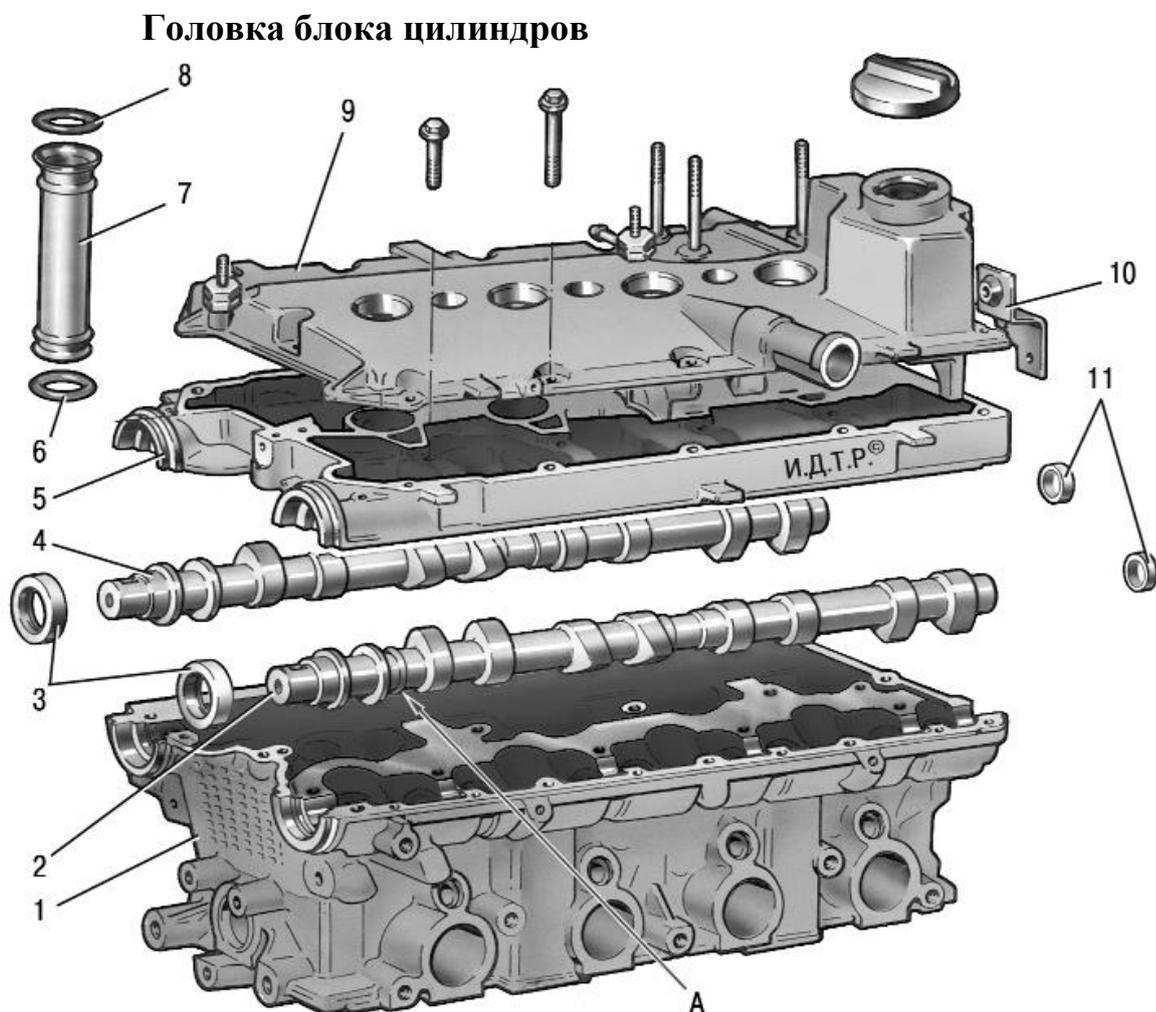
Детали головки блока цилиндров двигателя ВАЗ-2112: 1 – головка блока; 2 – впускной распределительный вал; 3 – сальник; 4 – выпускной распределительный вал; 5 – корпус подшипников распределительного вала; 6, 8 – уплотнительные кольца; 7 – направляющая труба; 9 – крышка головки блока; 10 – кронштейн крепления жгута проводов;
